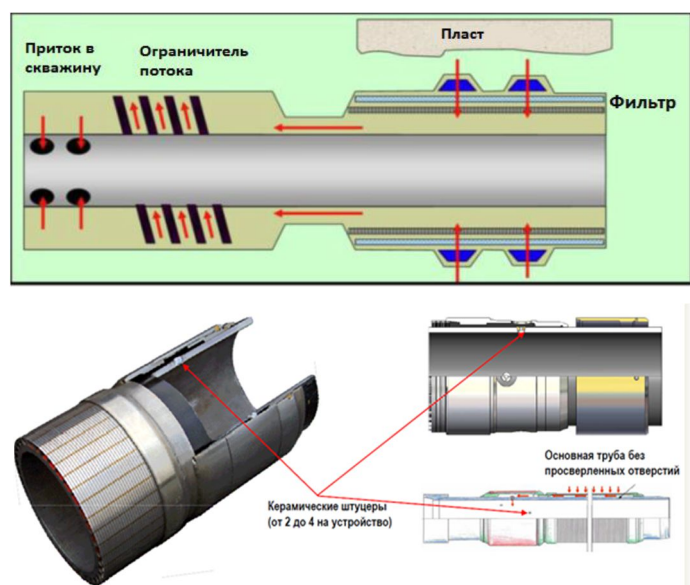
Схематичное представление устройств контроля притока штуцерного типа
